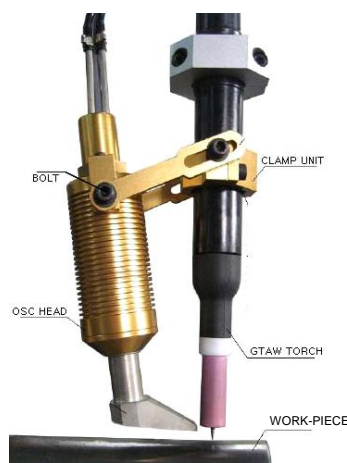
Exemplo de equipamento (eletroímã) comercial para defletir arcos de soldagem (HANGIL, 2009)
